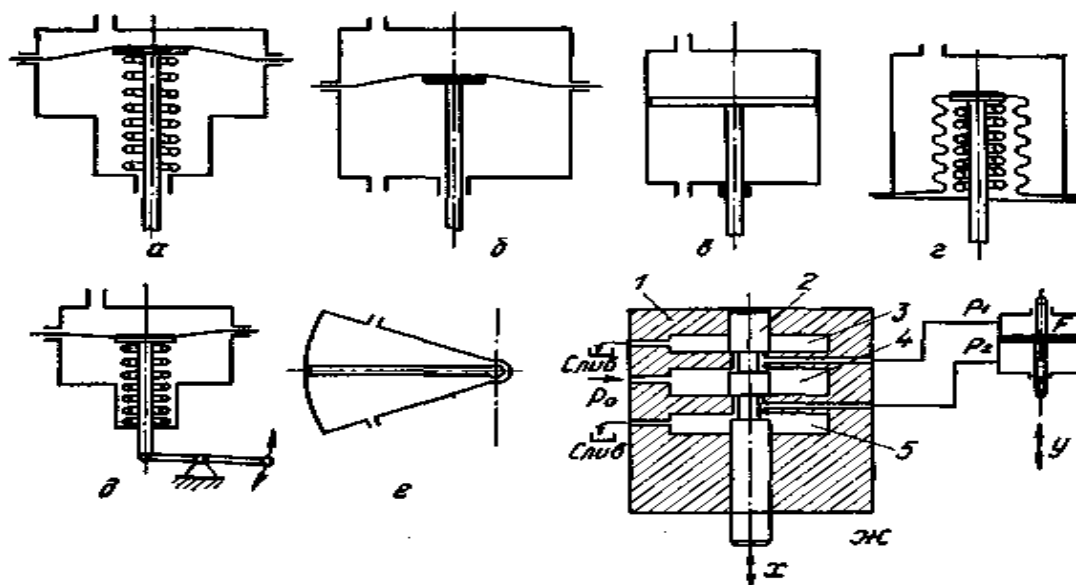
Схемы пневматических и гидравлических исполнительных механизмов: а - мембранный с пружиной; б - мембранный без пружины; в - поршневой; г - сильфонный; д - мембранный поворотный; е - лопастный; ж - гидравлический ИМ с золотником
